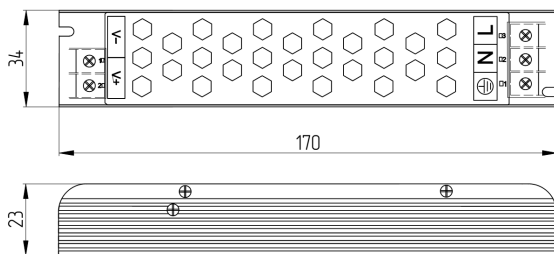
Габаритные размеры блока питания Geniled GL-12V60WM20 Slim.
